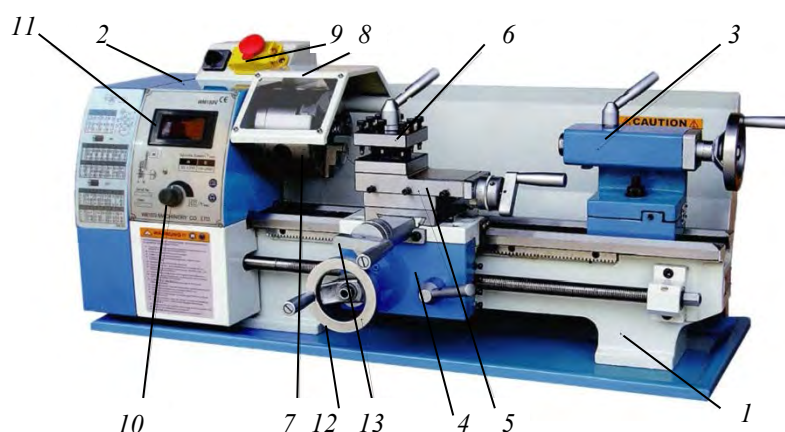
Общий вид токарного настольного станка Universal WM180V
